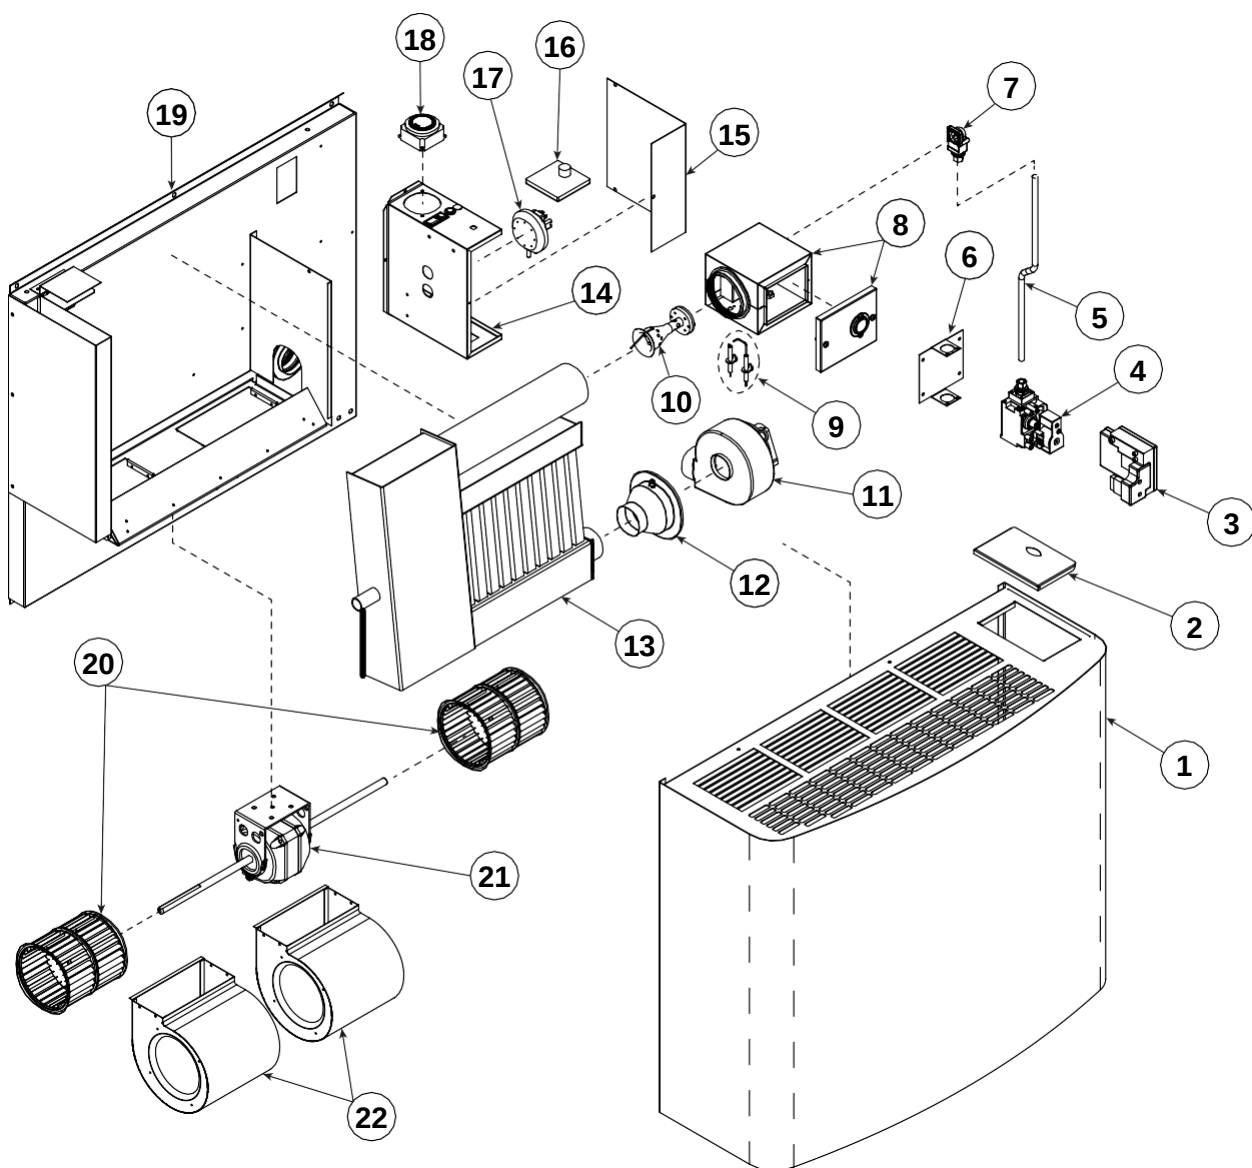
Vedere explodată a modelului KING 70 FE
